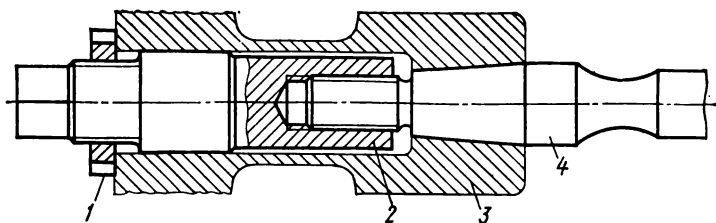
Приспособление для зажатия цилиндрических образцов на консольный изгиб:
